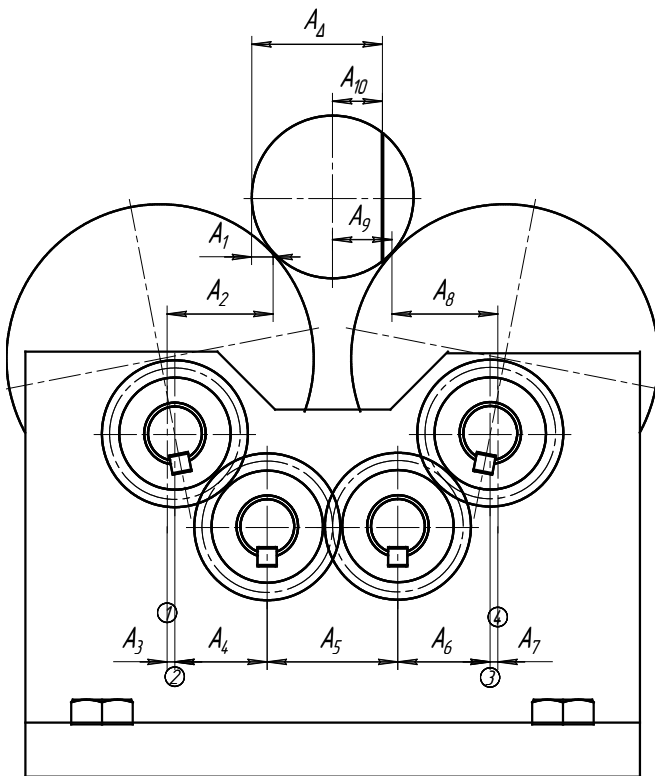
Базуюча призма (патент України № 31416) і розмірний ланцюг для визначення похибки базування вала при фрезеруванні лиски, перпендикулярної до робочої поверхні стола верстата
